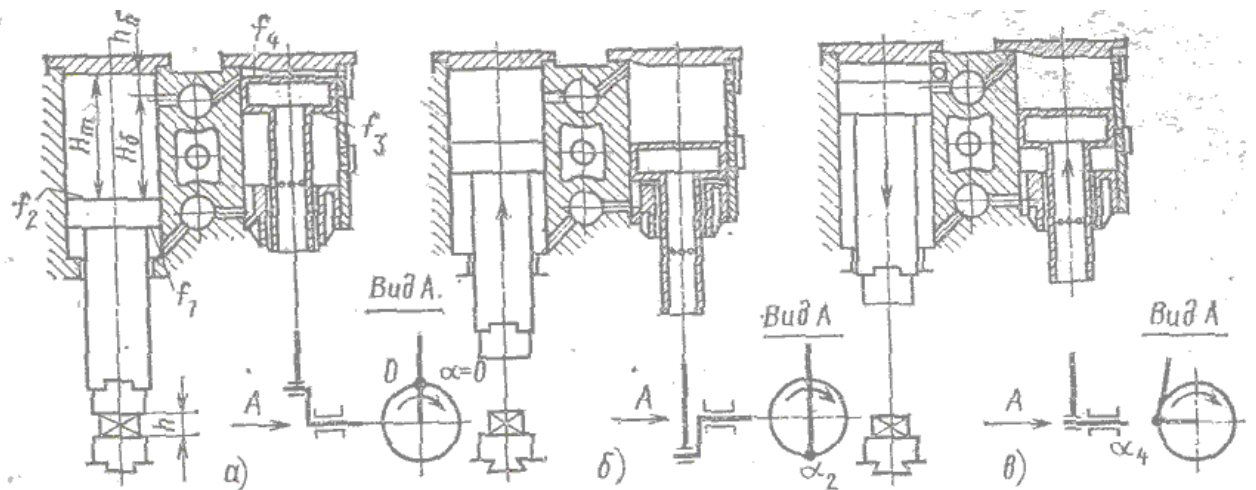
Схема движения поршней рабочего и компрессорного цилиндров [2]:
